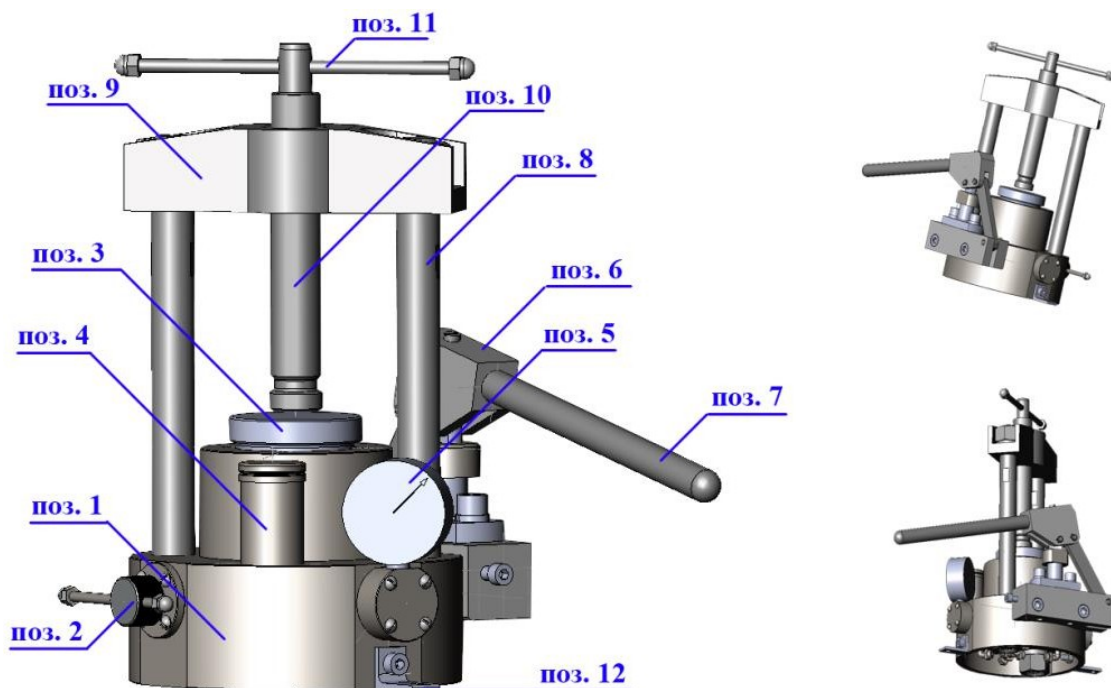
Устройство прессы: 1 – корпус; 2 – выпускной винт; 3 – пятка; 4 – бак; 5 – манометр; 6 – ручной насос; 7 – ручка насоса; 8 – колонны; 9 – переключатель; 10 – прижимной винт; 11 – ручка винта; 12 – кронштейн.
